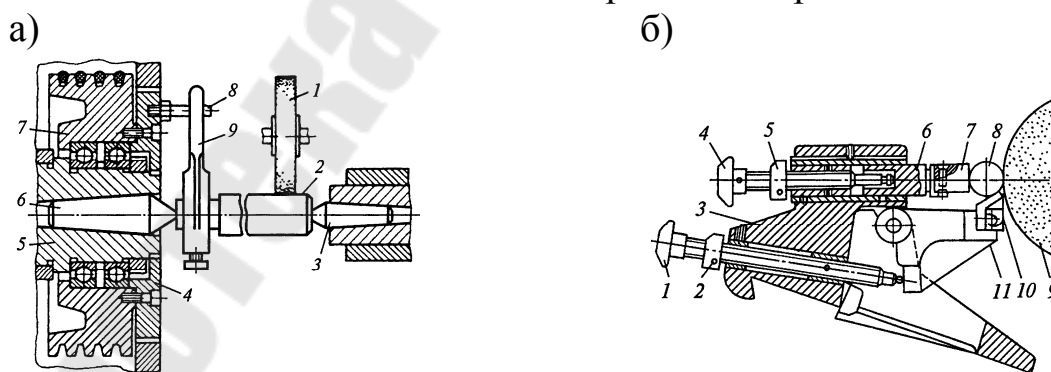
Устройства для установки и закрепления заготовок:
